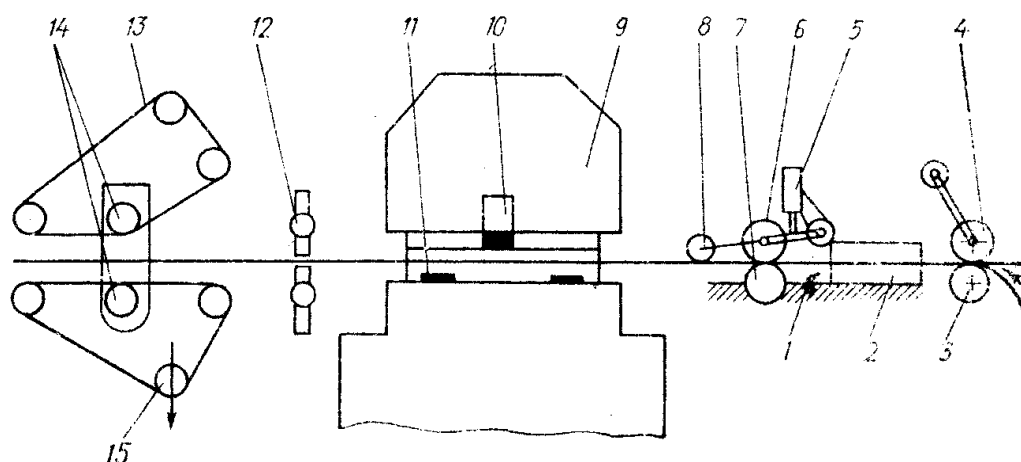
Схема подачи картонного полотна в штанцевальный аппарат и механизм выдачи листов с высечками: 1 – направляющий стол; 2 – направляющая линейка; 3 – ведущий валик; 4 – направляющие валики; 5 – пневматический цилиндр; 6 – прижимные ролики; 7 – приводные ролики; 8 – устройство для снятия электростатического заряда; 9 – штанцевальный аппарат; 10 – пневматический зажим рамы в верхнем штанцевальном тигле; 11 – рама со штампом; 12 – подающее приспособление; 13 – ленточный конвейер; 14 – зажимные ролики; 15 – натяжной валик
